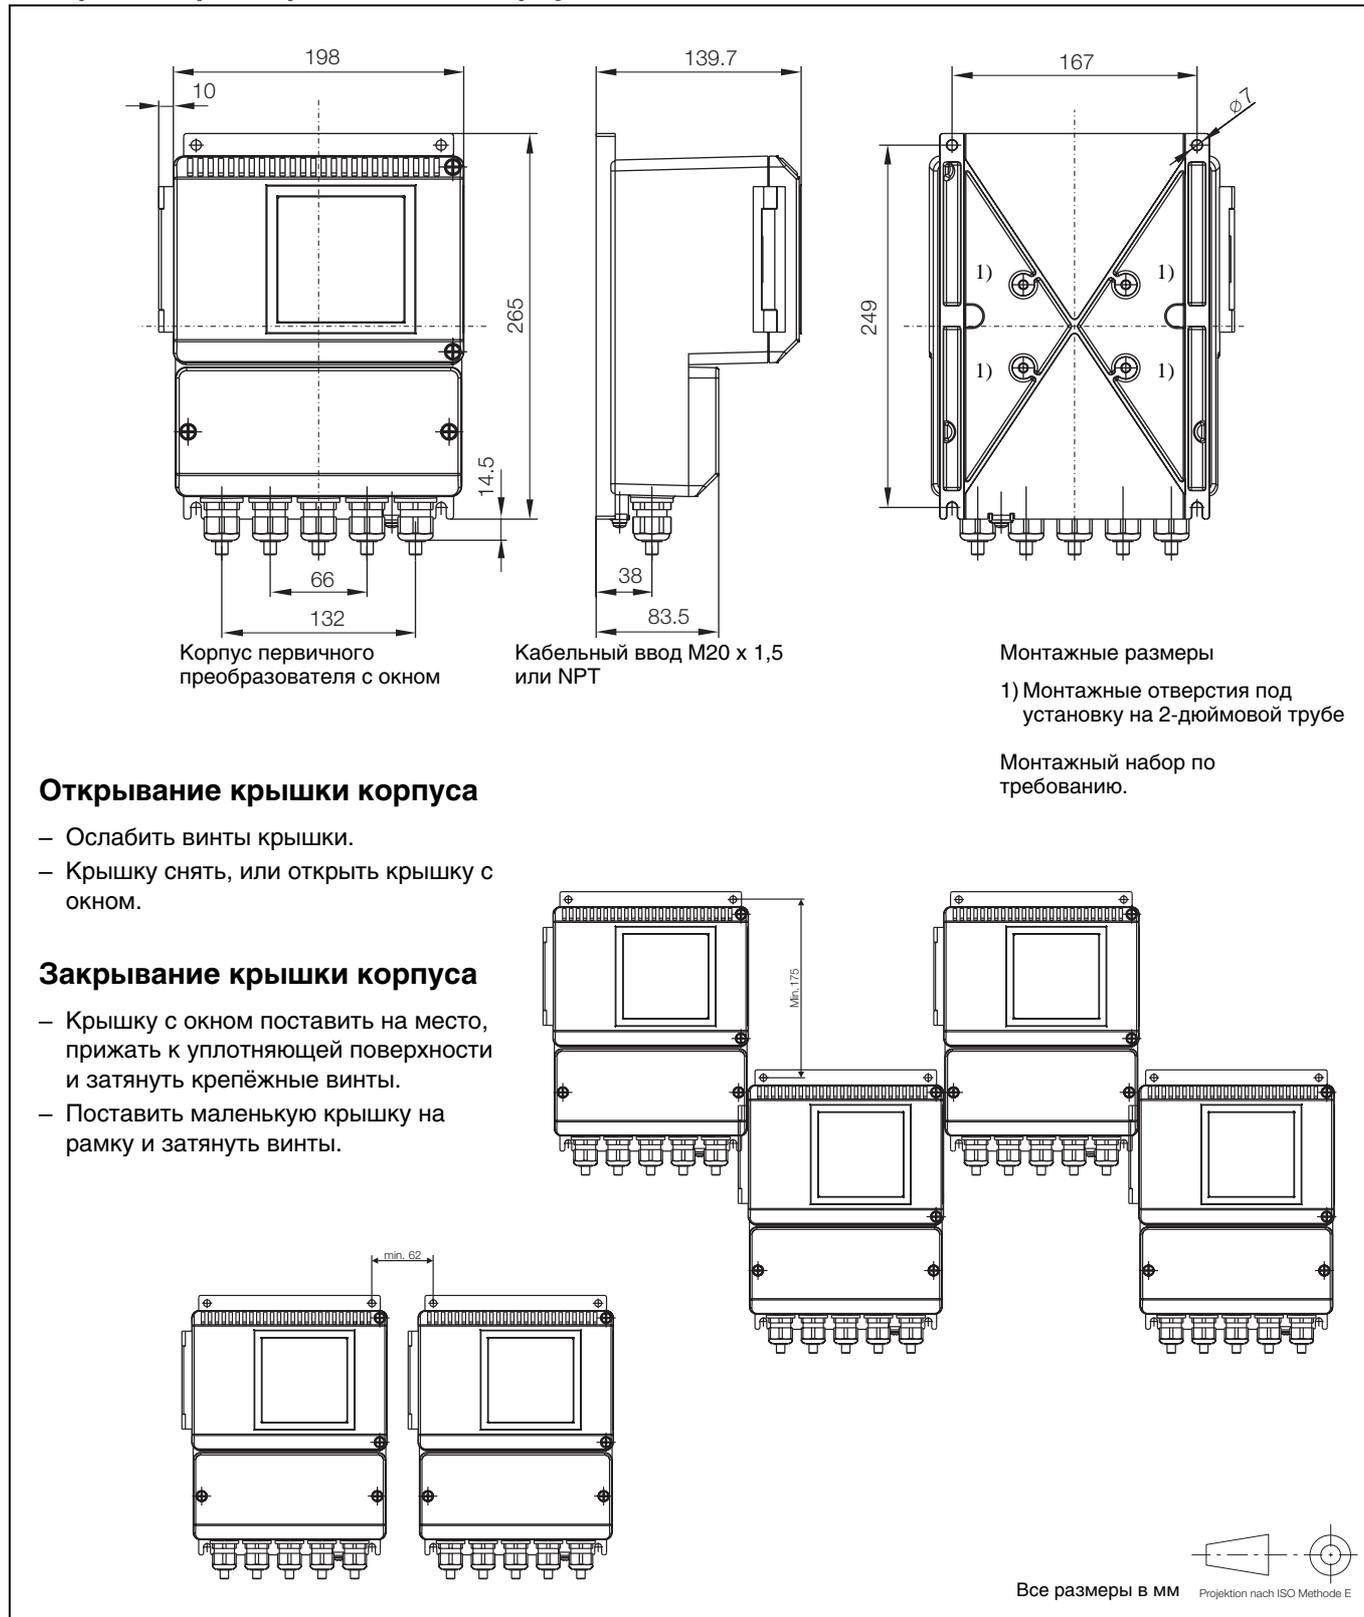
Габаритные размеры вторичного преобразователя и установка крышки
